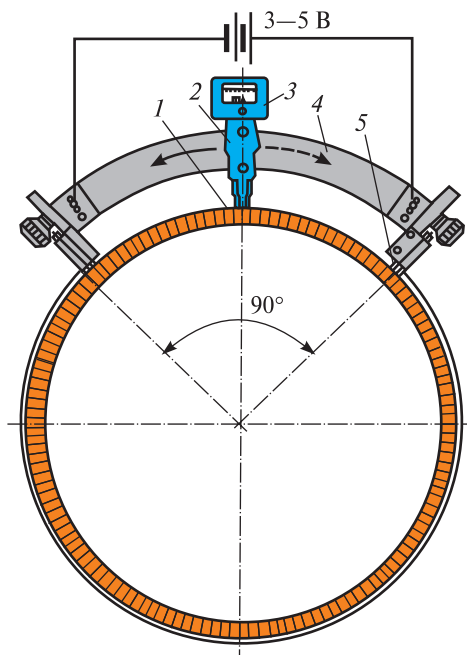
Приспособление для проверки якореj на межвитковое замыкание:
